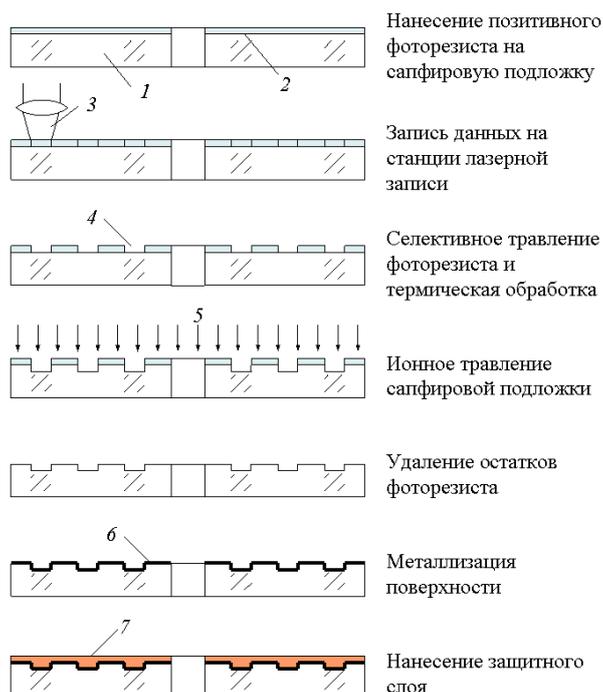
Схема процесса изготовления оптического носителя для долговременного хранения данных [8, 9]: 1 — подложка; 2 — слой позитивного фоторезиста; 3 — сфокусированный лазерный луч; 4 — окно в слое фоторезиста; 5 — ионный пучок; 6 — металлический отражающий слой; 7 — слой защитного лака.
